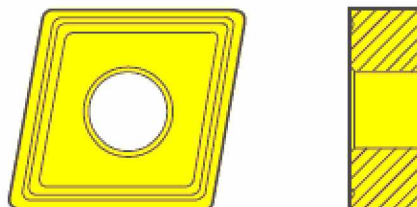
Ромбічна пластина для напівчистової обробки CNMG120404-M1
